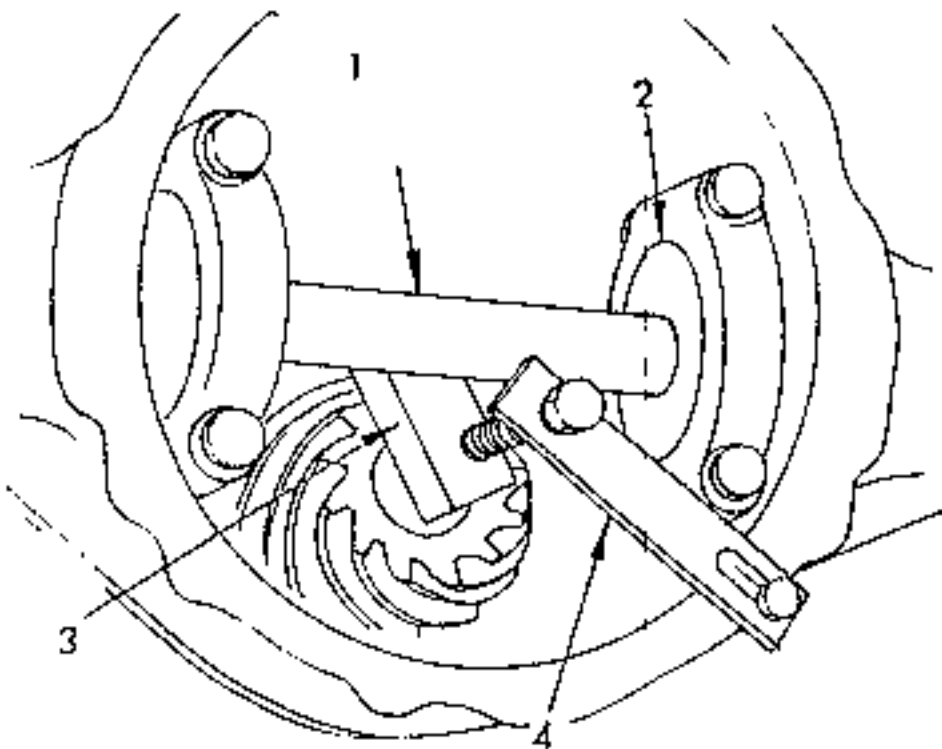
Spezialwerkzeuge zum Einstellen der Kegelradtiefe, im Hinterachsgehäuse eingesetzt.
